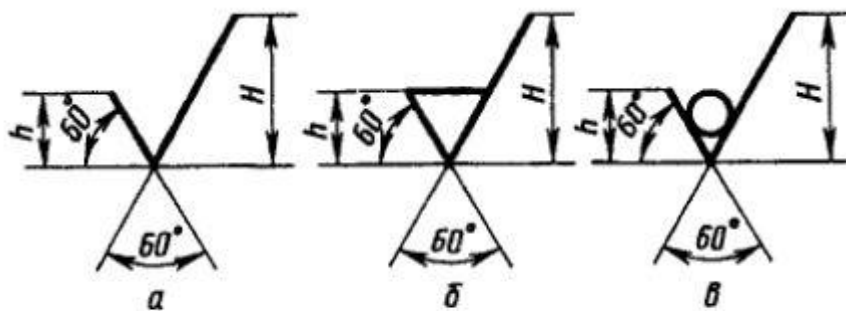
Знаки для обозначения шероховатости поверхности
